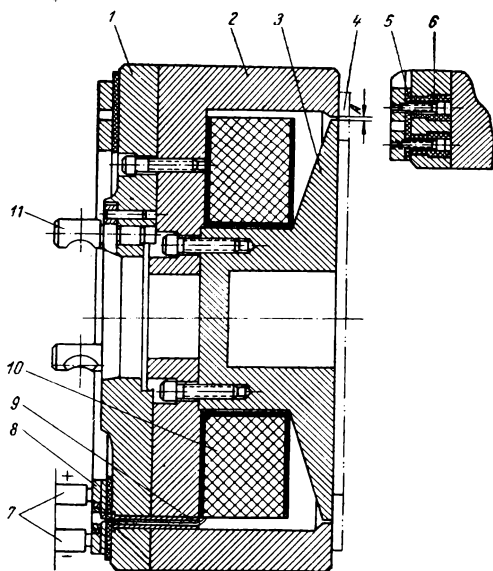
Установка обрабатываемой детали (кольцо) на магнитном патроне.
